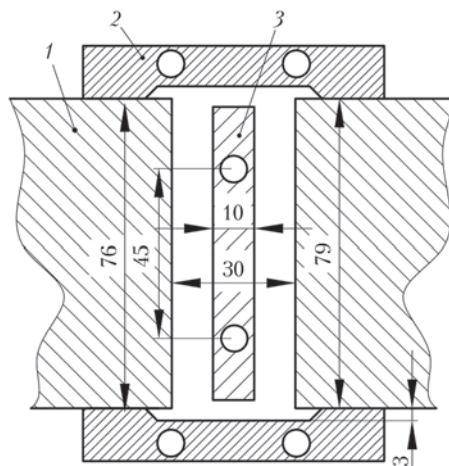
Геометрические параметры сборки изделий под ЭШС: 1 — свариваемые изделия; 2 — водоохлаждаемая формирующая планка (ползун); 3 — мундштук
